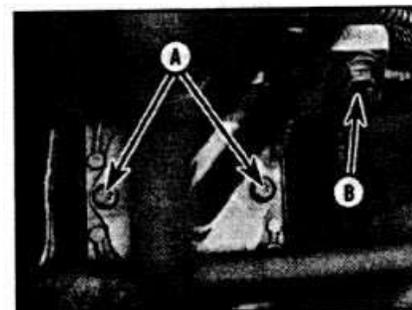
Е.28. Расположение винтов крепления трубопровода "А" и болт крепления корпуса фильтра "В".
